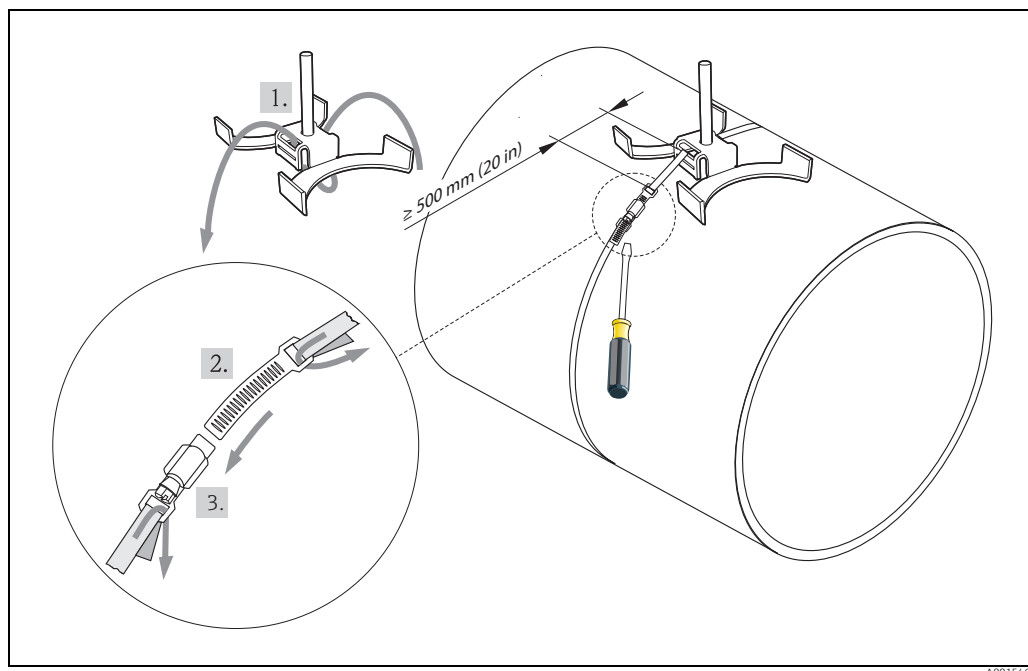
Предварительный монтаж крепежных лент на трубопроводах DN > 600 (24 дюйма)
